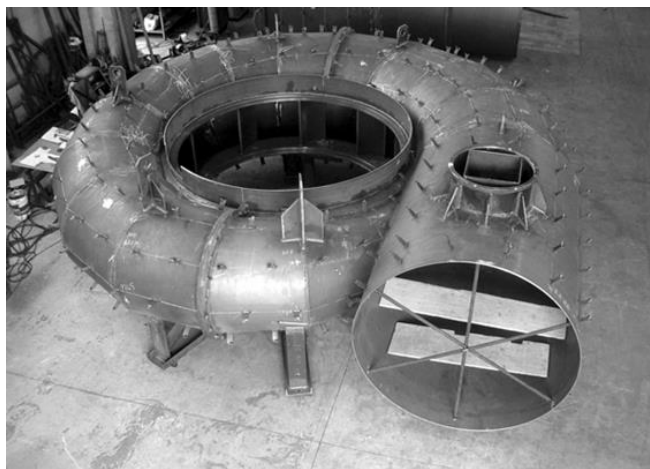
Cámara espiral. Fuente: Ramón Abella Monserrat.
